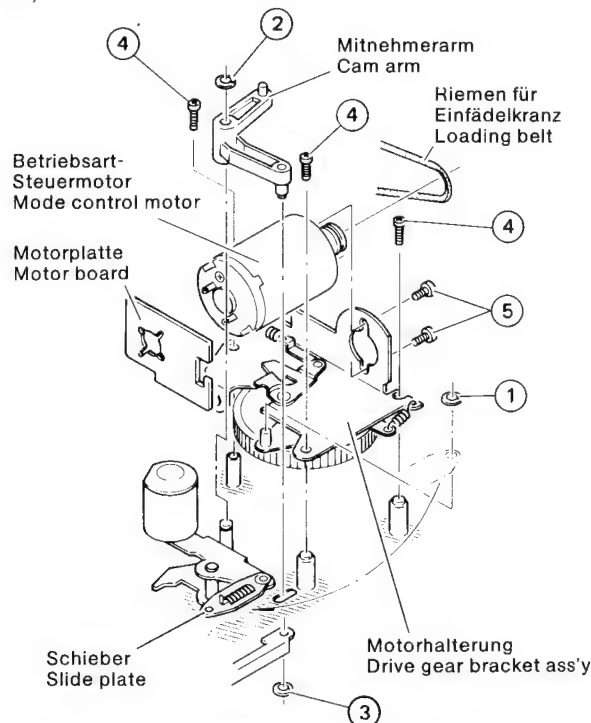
Ausbau des Betriebs-Steuermotors /
